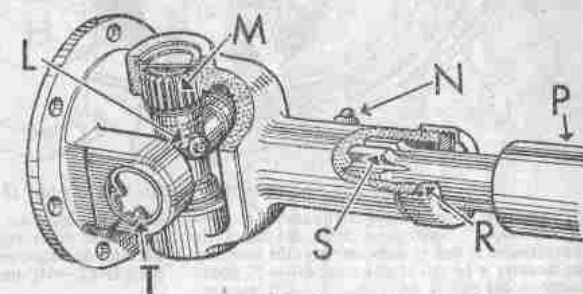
Junta cardan con árbol deslizante... y cojinetes de agujas...
